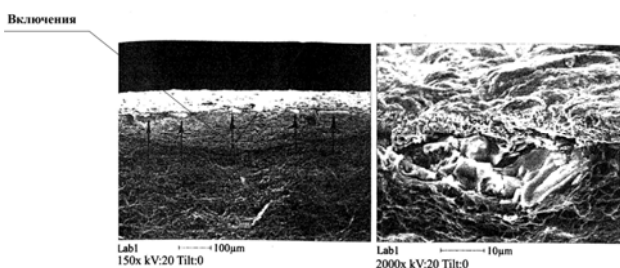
Включения корунда на поверхности исходной заготовки рабочей лопатки компрессора под слоем меди (до нагрева под выдавливание)
